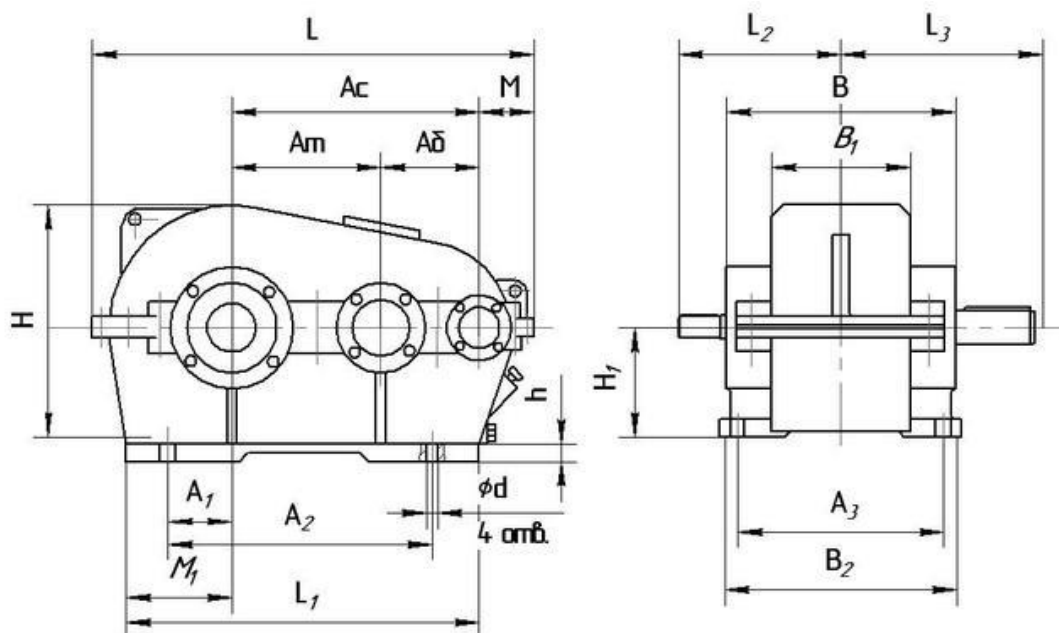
Габаритні та приєднувальні розміри редуктора
